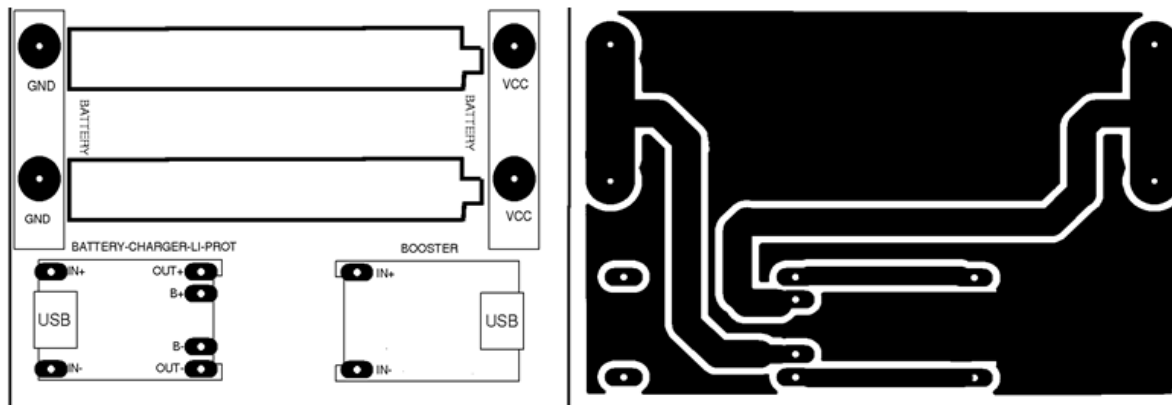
PCB del sistema de alimentación ininterrumpido, lado de componentes (izquierda) y lado de pistas (derecha)
